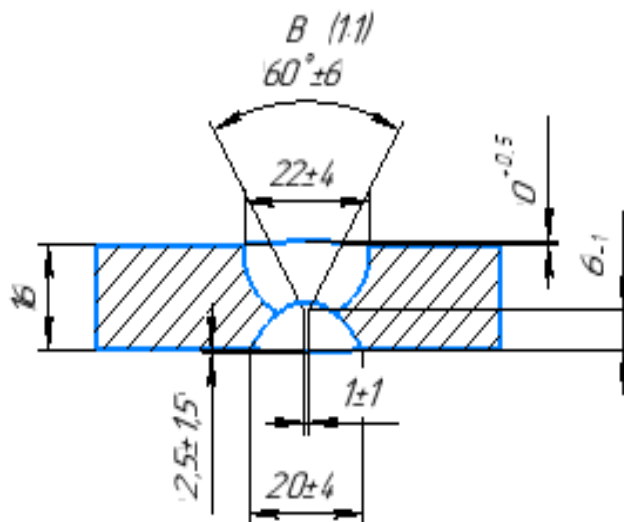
Загальний вигляд стикового зварного з'єднання
